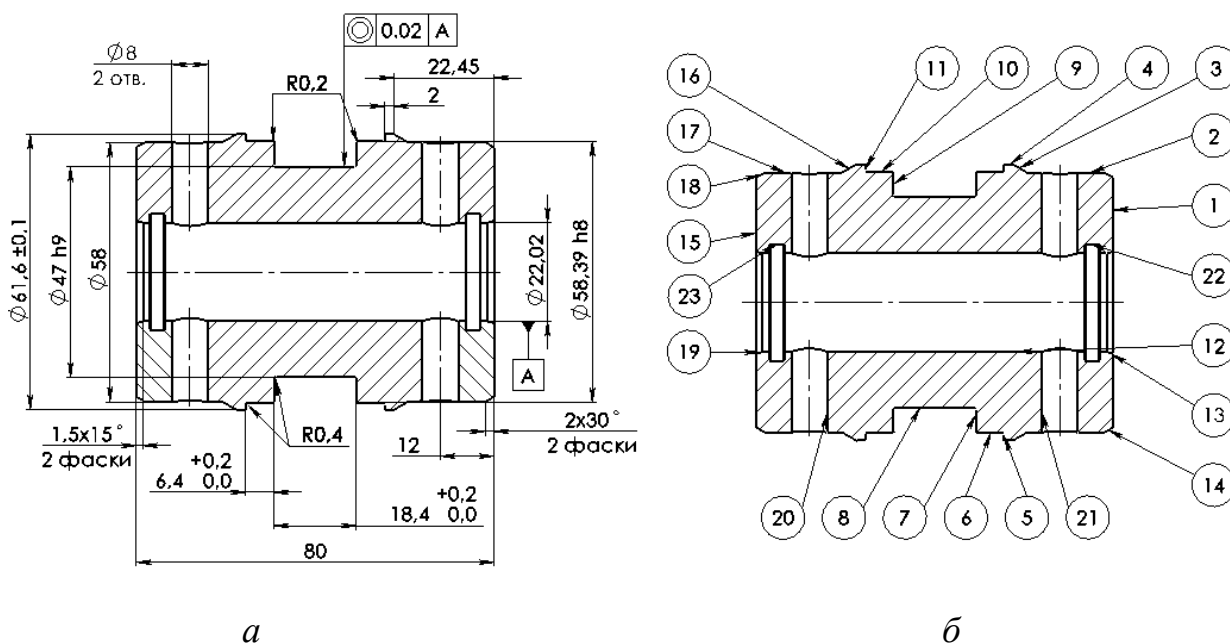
Креслення поршня гідроциліндра *a* та оброблювані поверхні *б*.
